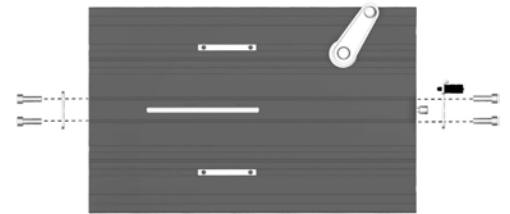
Die Einstellleistenhalterungen sind mit jeweils zwei Schrauben befestigt.
